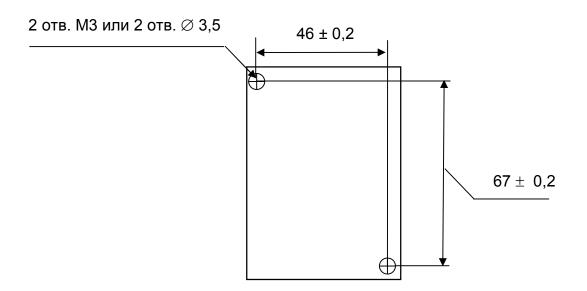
Габаритные и установочные размеры ИП в корпусе 60х85х75 mm с креплением на DIN – рейку (35 mm)
